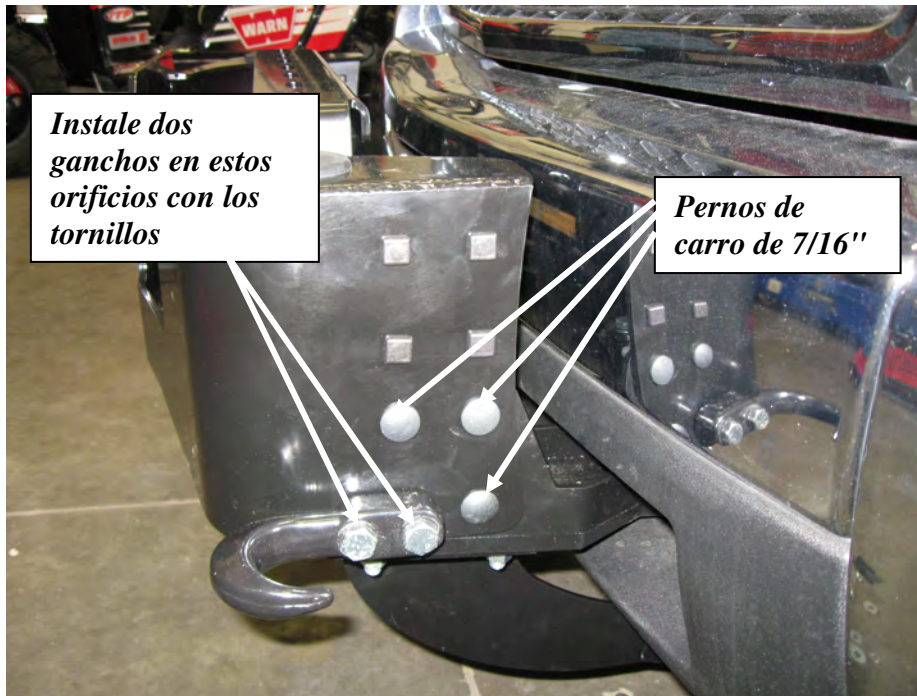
Placa de extensión del bastidor izquierda instalada. El Sierra es similar
